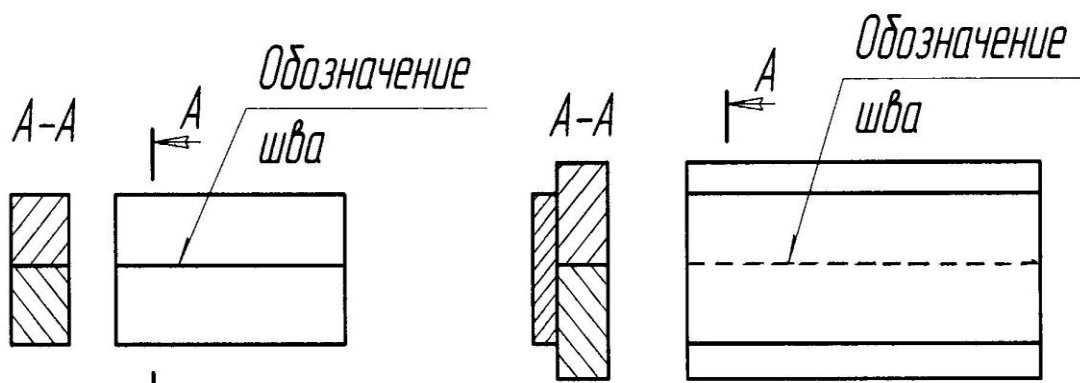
Пространственное расположение сварных швов
